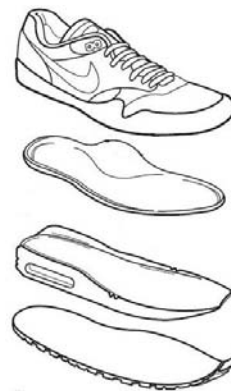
Du haut en bas, la tige, la semelle interne, la semelle intermédiaire et la semelle externe de la chaussure [50]
